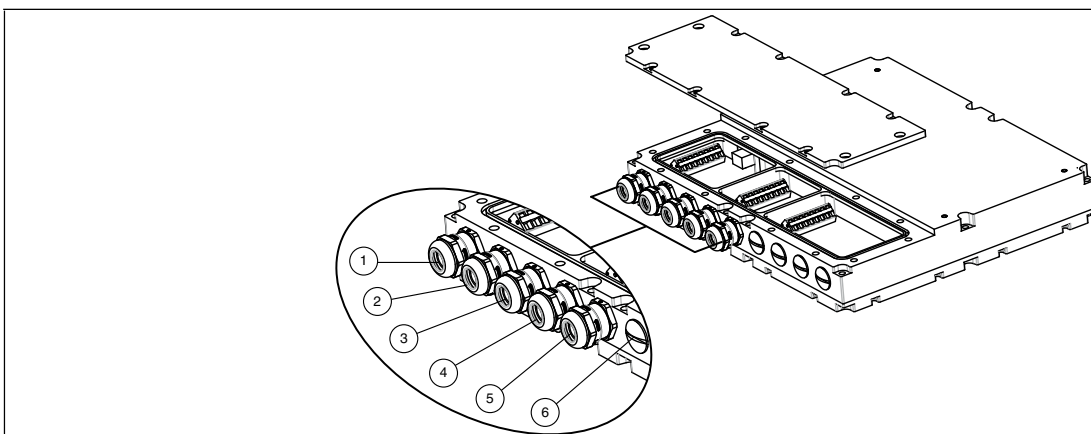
Dimensionierung der Kabelverschraubungen
